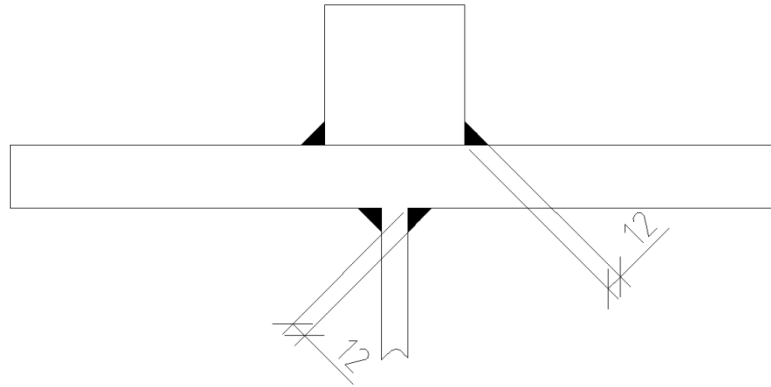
Pormenor dos cordões de soldadura (Perfil I da lança/contralança)
